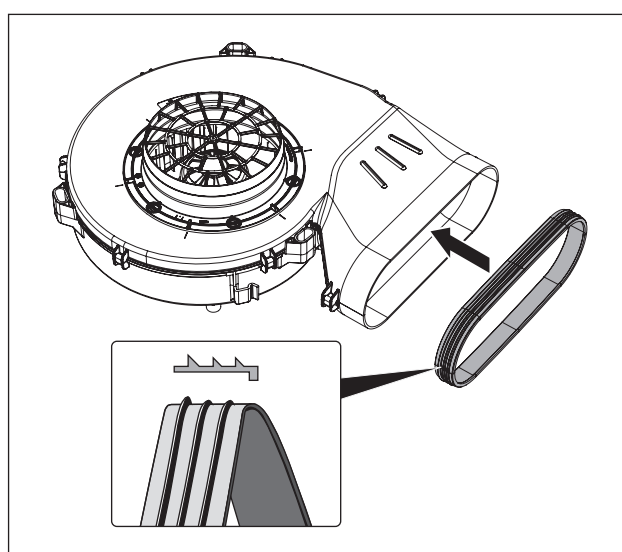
Aplicar a vedação na tubuladura de saída do ventilador de rodapé
